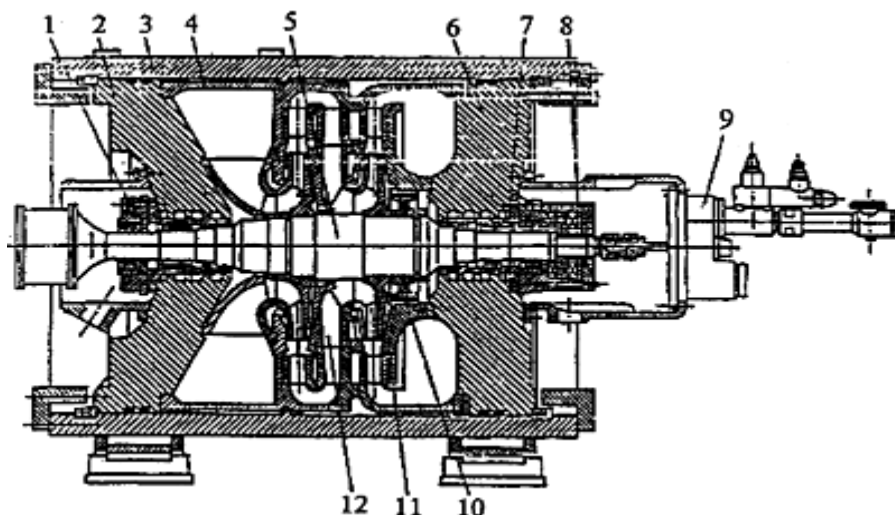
Полнонапорный двухступенчатый нагнетатель НЦВЭ
